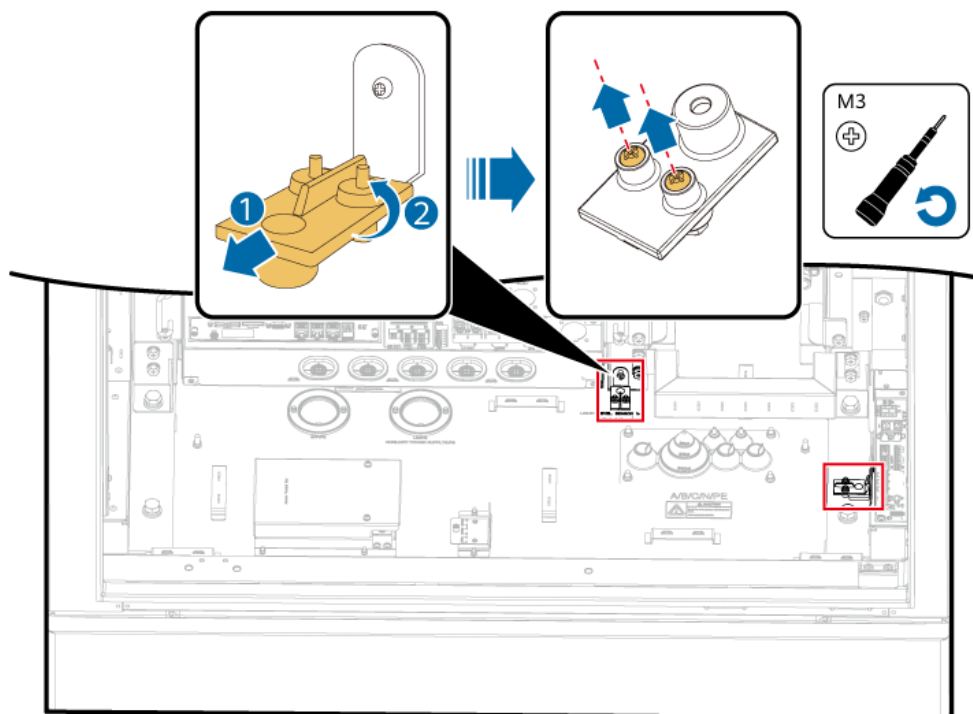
Entfernen des Ablenkblechs der Kabel
